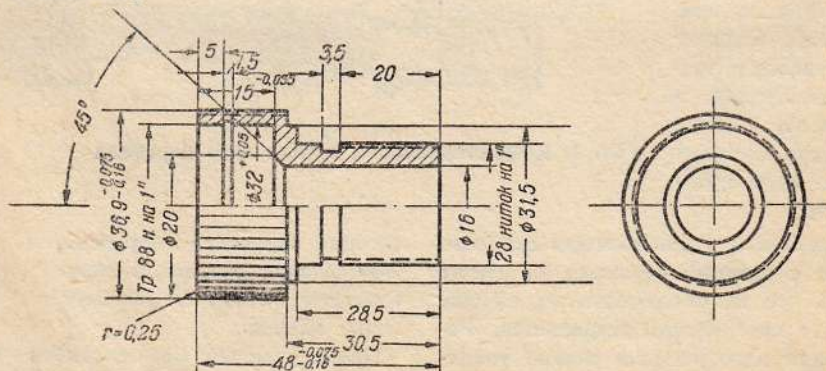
Втулка для шарикоподшипника вала барабана, ближайшего к барабану
